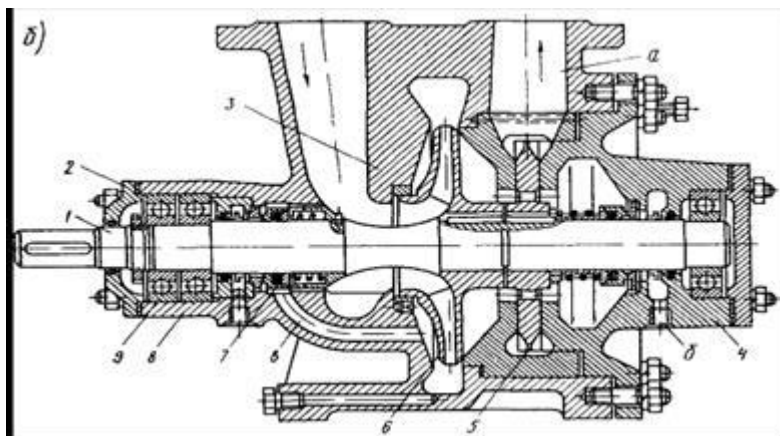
Центробежно-вихревой насос: 1-вал; 2-крышка; 3-корпус насоса; 4-8-корпус подшипников; 5-вихревое колесо; 6-центробежное колесо; 7-уплотнение; 9 - шариковый подшипник;
